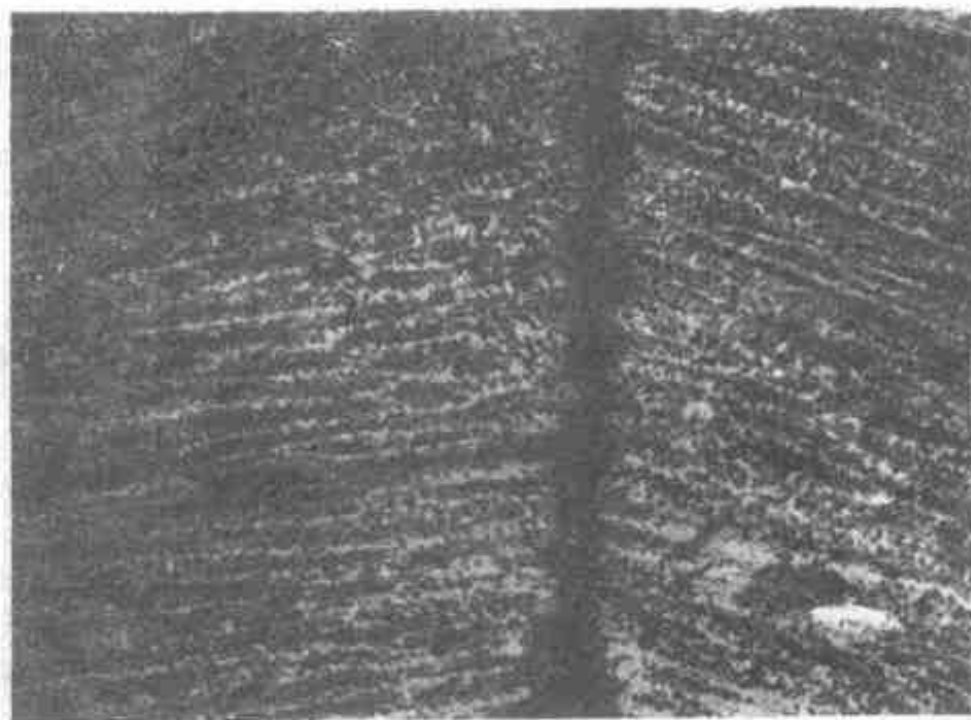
焊缝横断面中心线结晶裂纹
